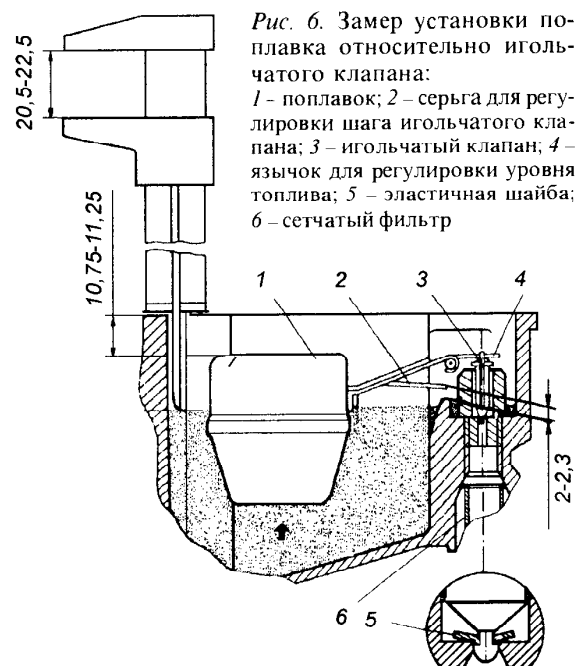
Замер установки поплавка относительно иглычатого клапана:
